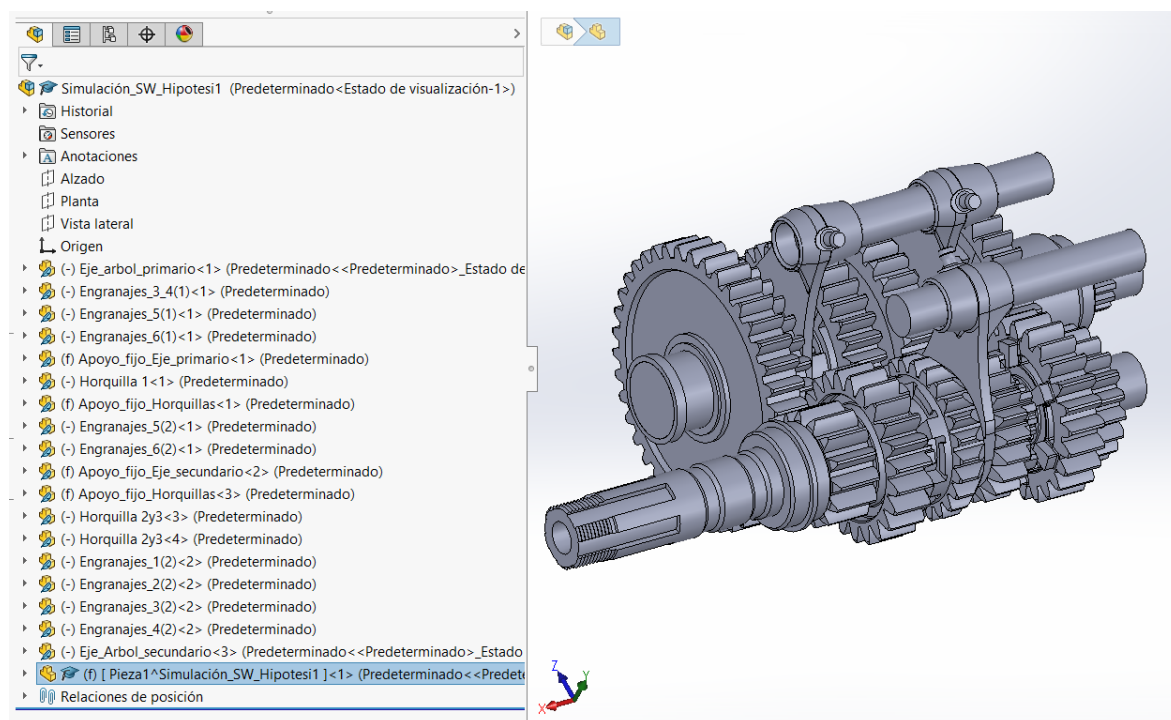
Ensamblaje cambio de marchas sin tambor (Fuente: propia)
